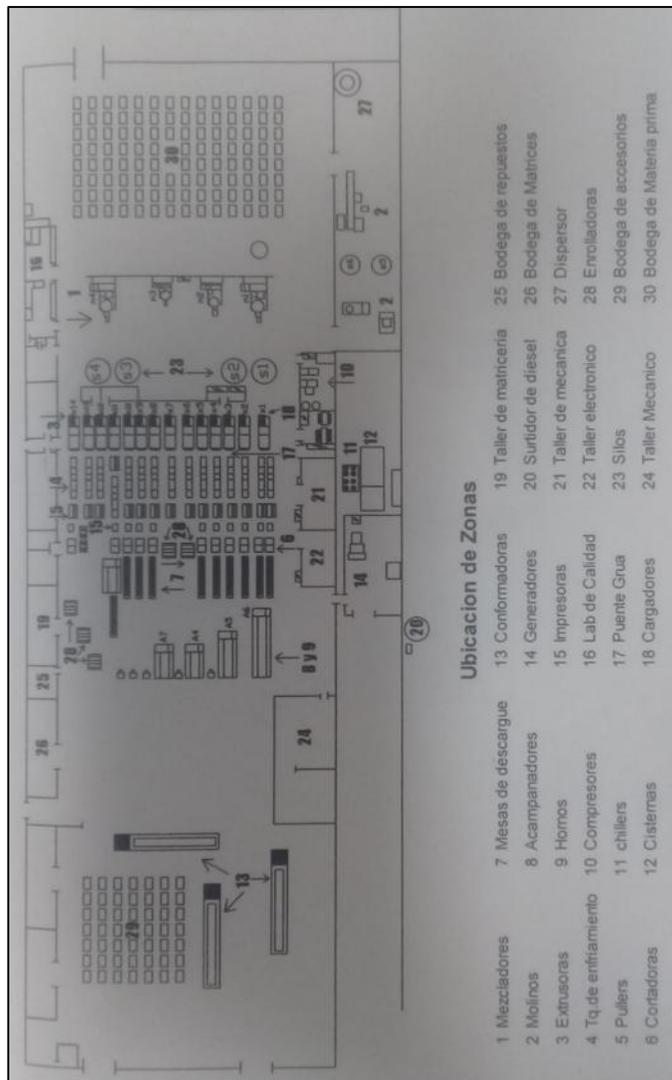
2 Ubicación de Zonas de maquinarias en la Planta de Producción N°1
